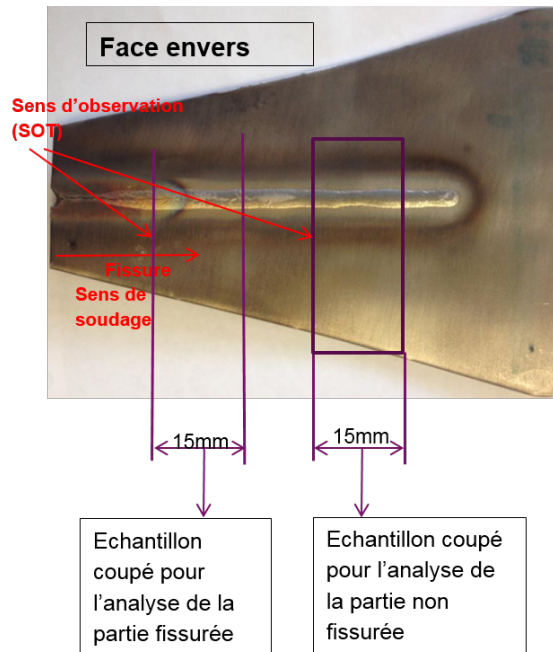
Plan de découpe pour éprouvette fissurée (réf. 1)
